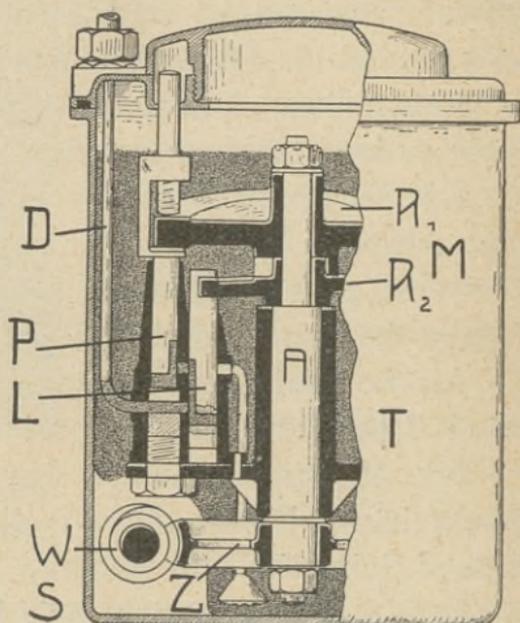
Querschnitt der Bosch-Oelpumpe.
